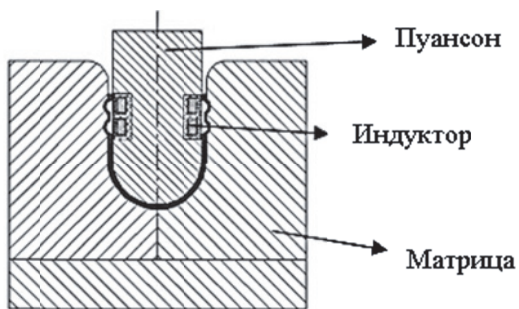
Схема магнитно-импульсной формовки на боковой поверхности полый детали
